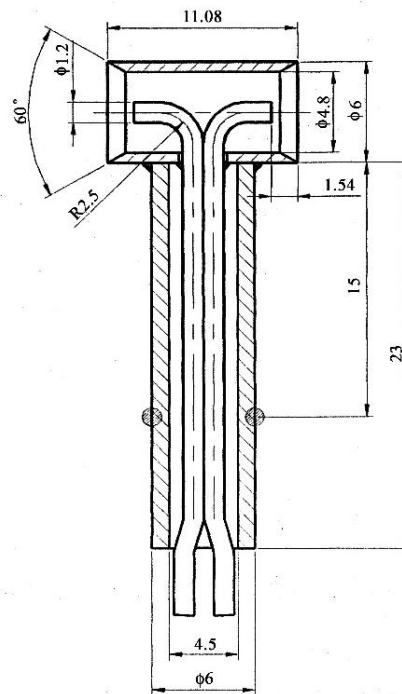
Т-подібний екранований насадок швидкості (ТЕНШ)
